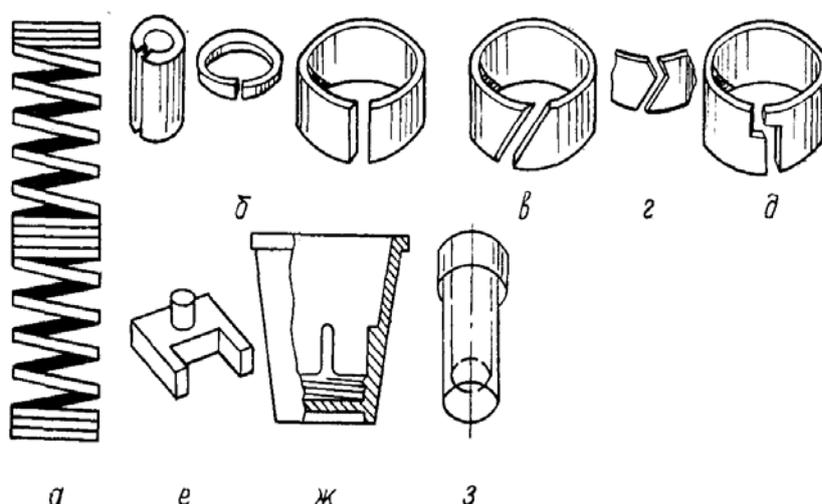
Технологические конструкции деталей, исключающие их сцепление в загрузочно-транспортных устройствах
